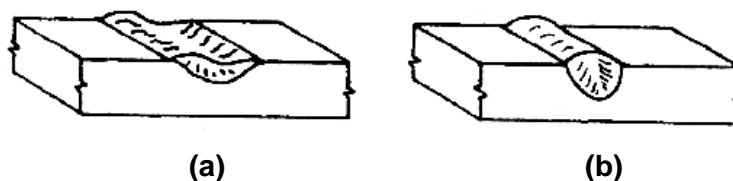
Efecto de la inclinación del área de trabajo sobre la forma de la franja de soldadura: (a) Cuesta abajo y (b) Cuesta arriba (23)
